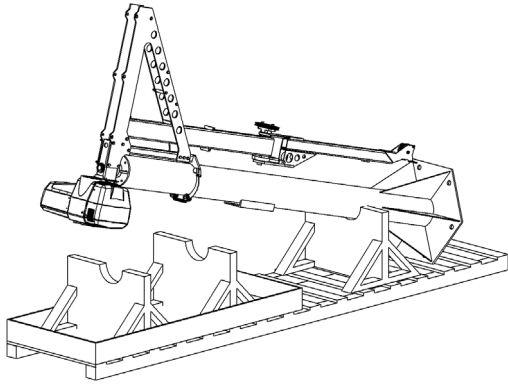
D. Rimozione del gruppo Easy Arm® dall'imballaggio.
